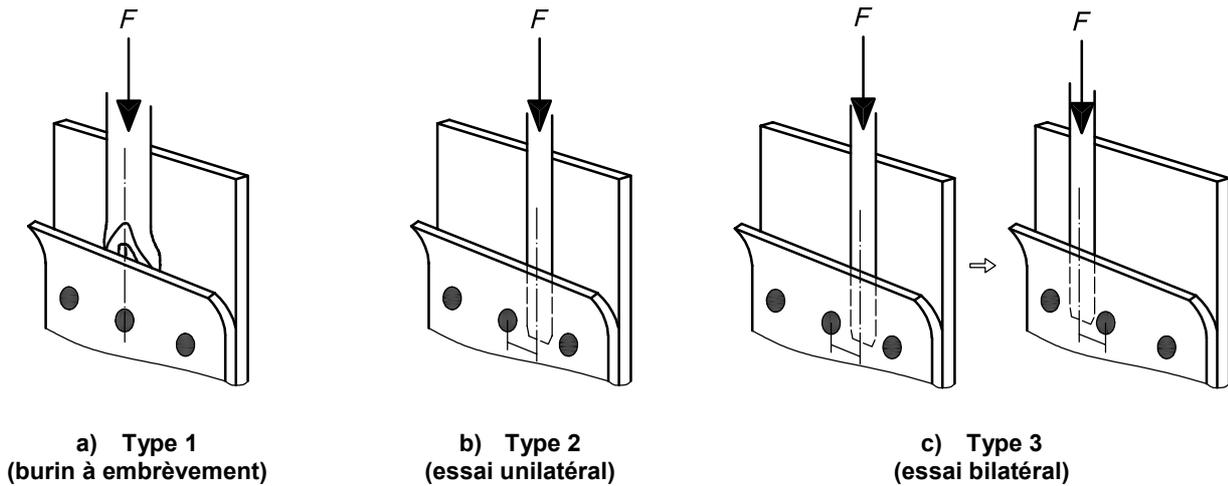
Essai de routine au burin sur joints soudés par résistance par points et par bossages
